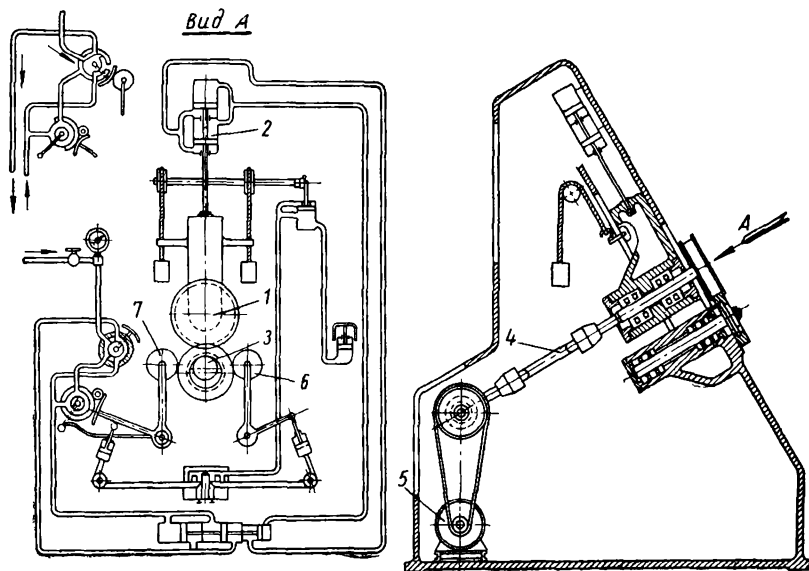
Принципиальная схема раскаточной машины МГР-250 и РМ-300М: 1 — вращающийся нажимной валок (бандаж); 2 — гидравлический цилиндр; 3 — центральный раскаточный валок; 4 — шарнирный вал; 5 — электродвигатель; 6 — направляющий ролик; 7 — контрольный ролик
